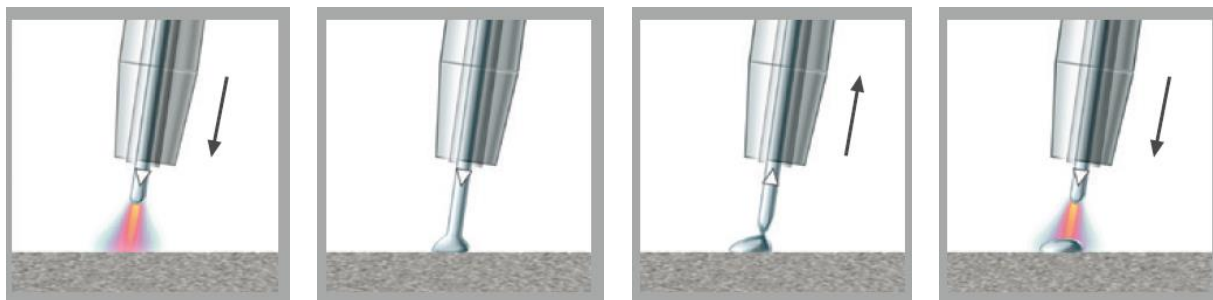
Principe de la soudure plasma PAW [16]
